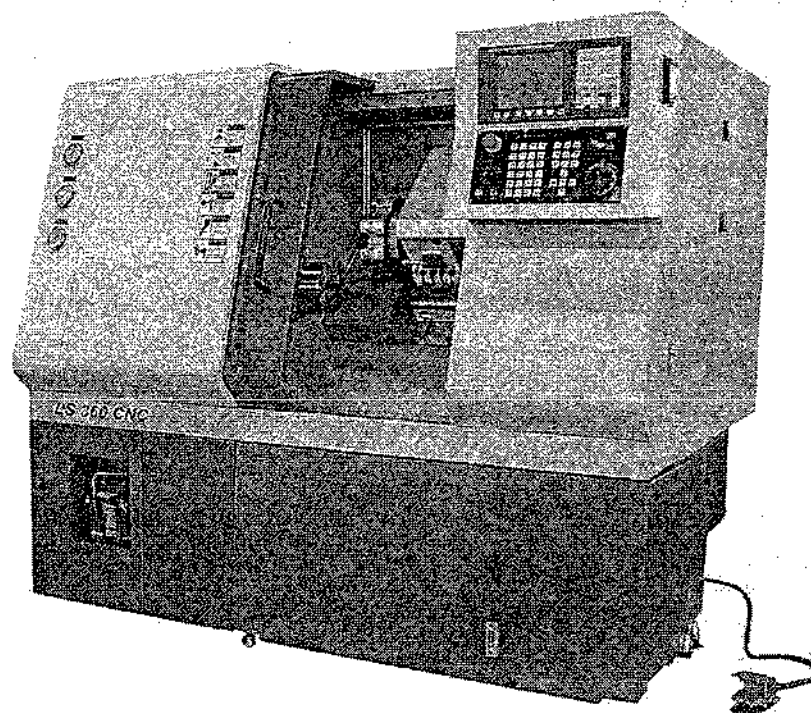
Токарный станок с ЧПУ MetalMaster LS360
